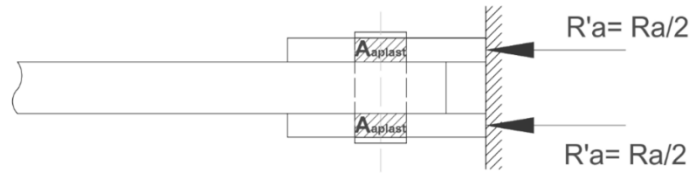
Carga en el eje pivote para esfuerzo por aplastamiento. Elaborado por: Galo Guañuna & Junior Ortiz
